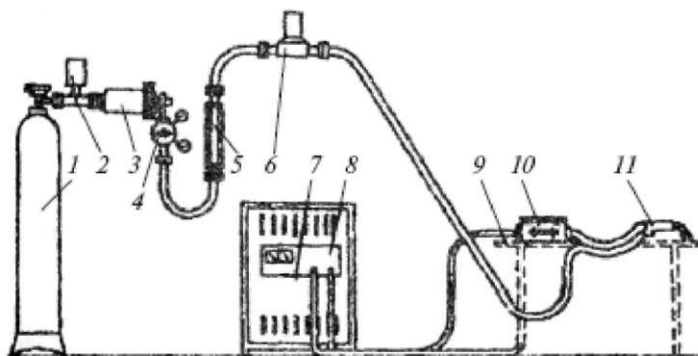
Пост для сварки в среде защитного газа: 1 - баллон с газом; 2 - подогреватель; 3 - осушитель; 4 - редуктор; 5 - расходомер (ротаметр); 6 - газозащитный клапан; 7 - источник питания; 8 - панель управления; 9 - рабочий стол; 10 - подающий механизм; 11 - горелка
